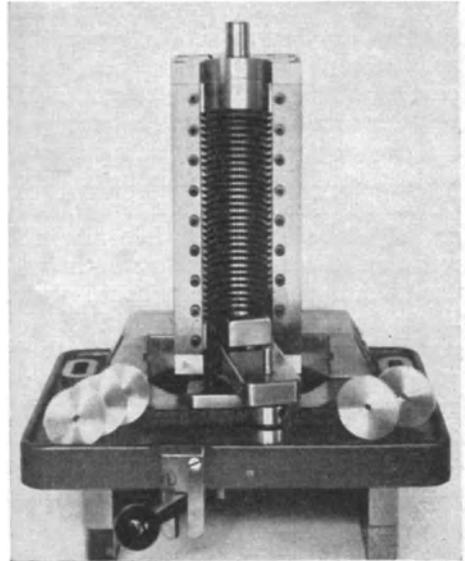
Ansicht des Räumzeuges Abb. 47 mit Räumvorrichtung.
